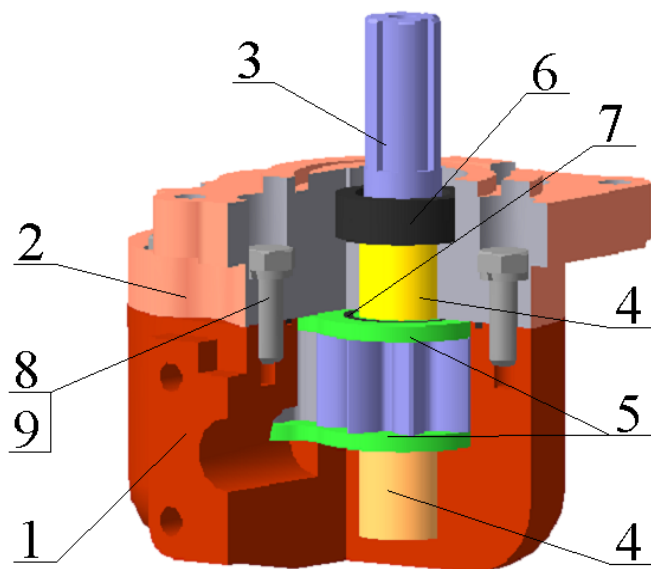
Шестеренный насос конструктивного исполнения «М» 1 – корпус; 2 – крышка;
